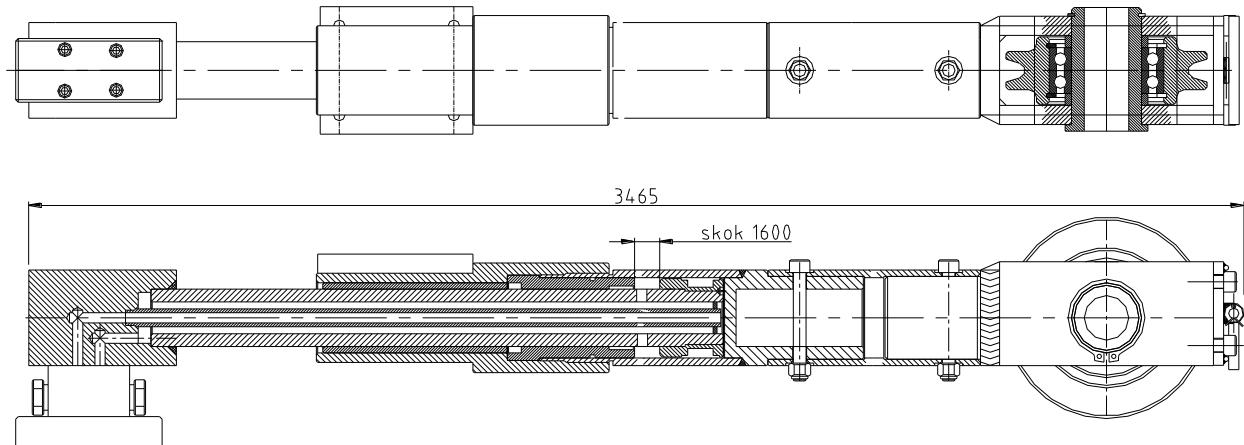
Zylinder mit Versorgung durch die Kolbenstange
